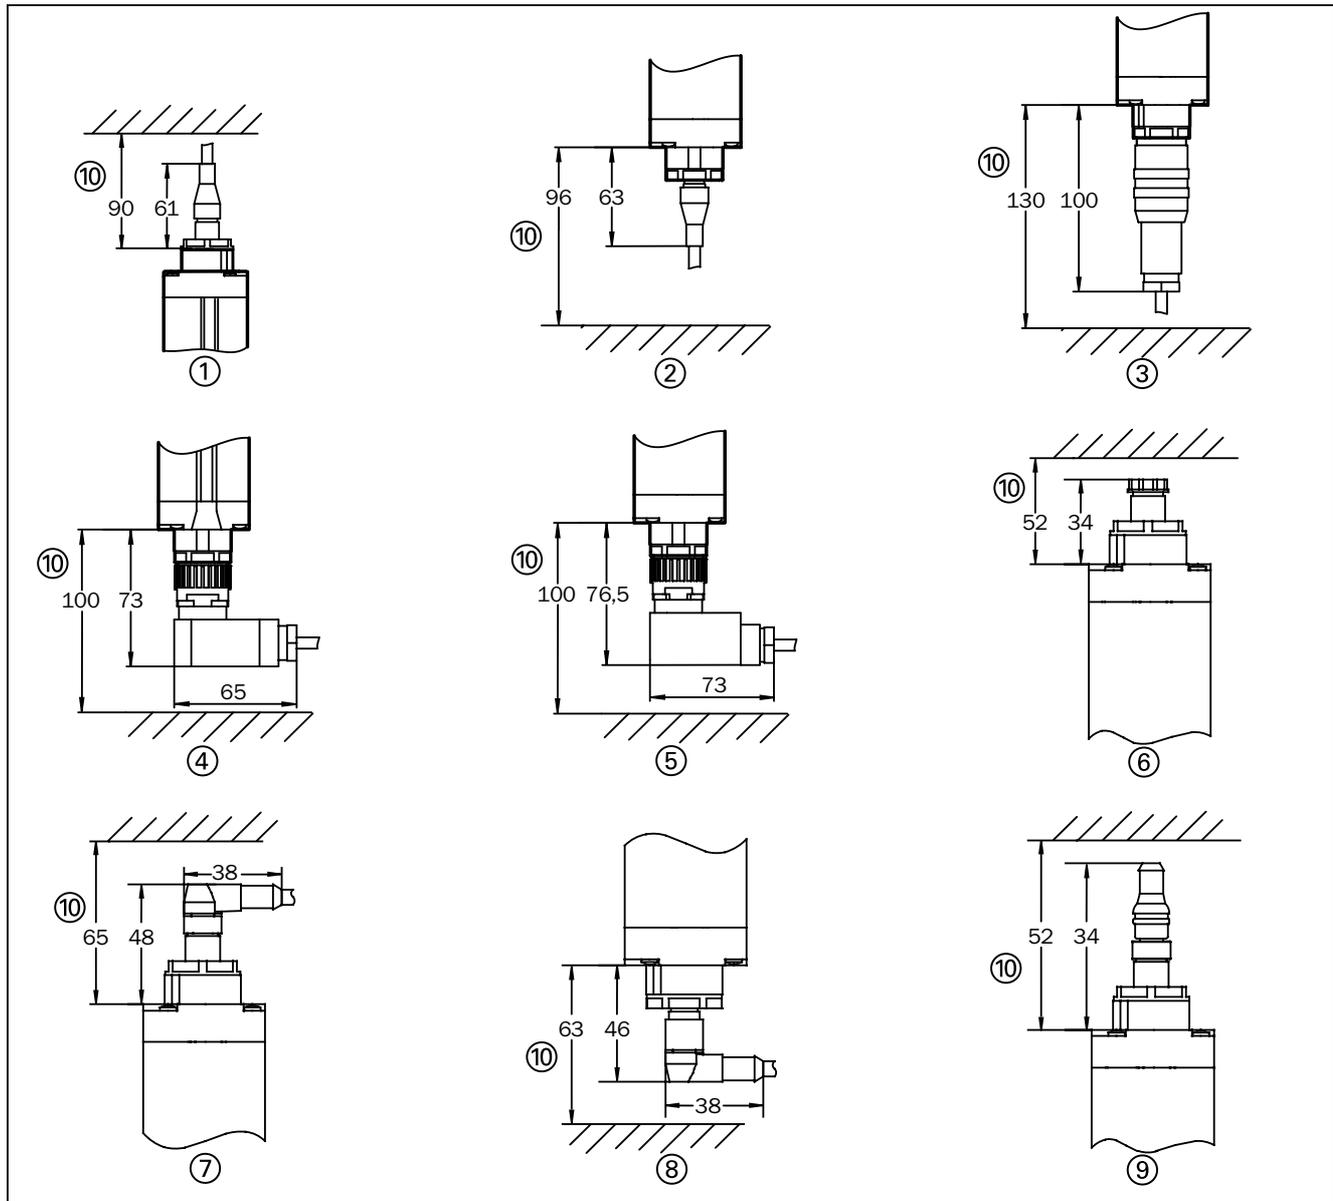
Plans et cotes d'encombrement des connexions pour les grands boîtiers
